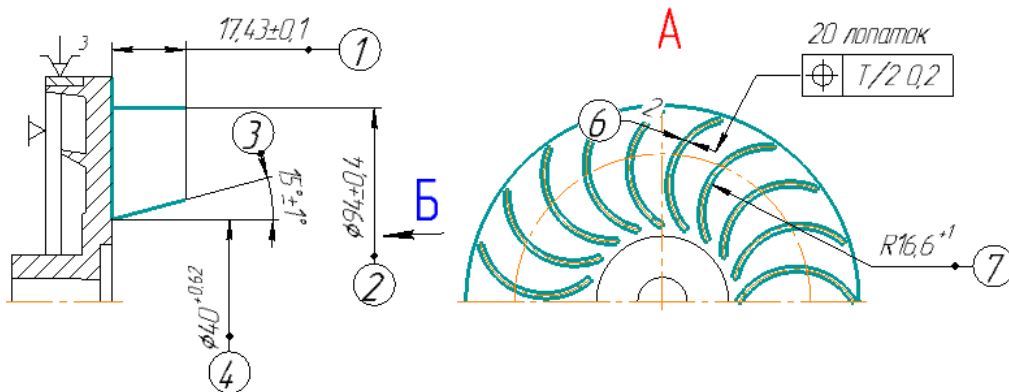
Эскиз 065 фрезерной операции с ЧПУ
